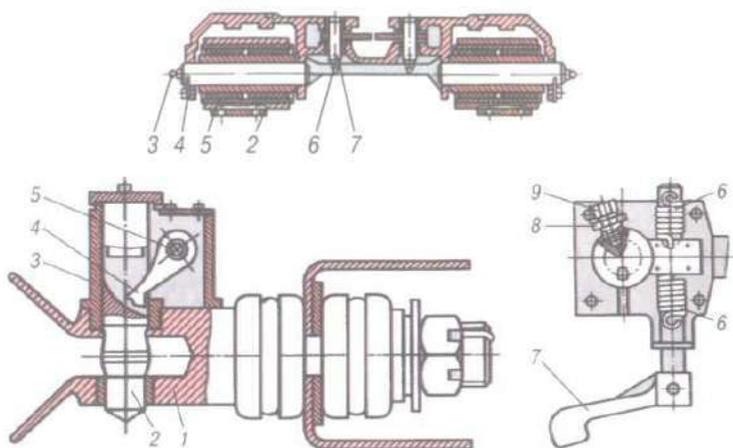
Тягово-зчіпний пристрій автомобіля КамАЗ-53212:
